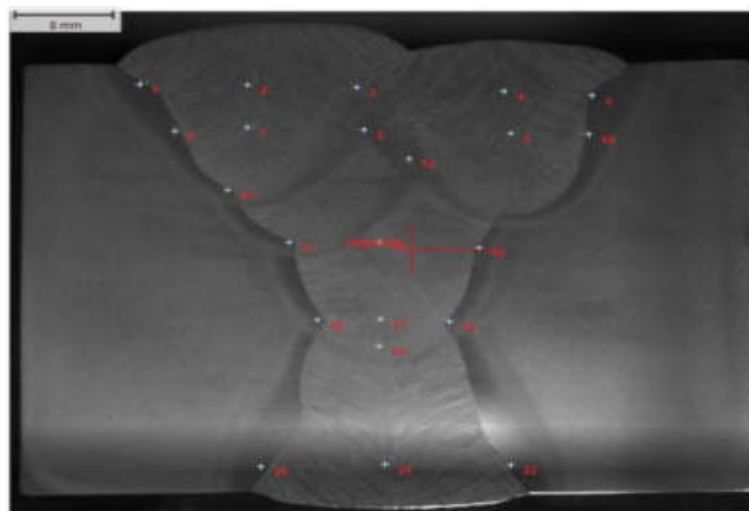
Шлиф после сварки с применением трех дуг
